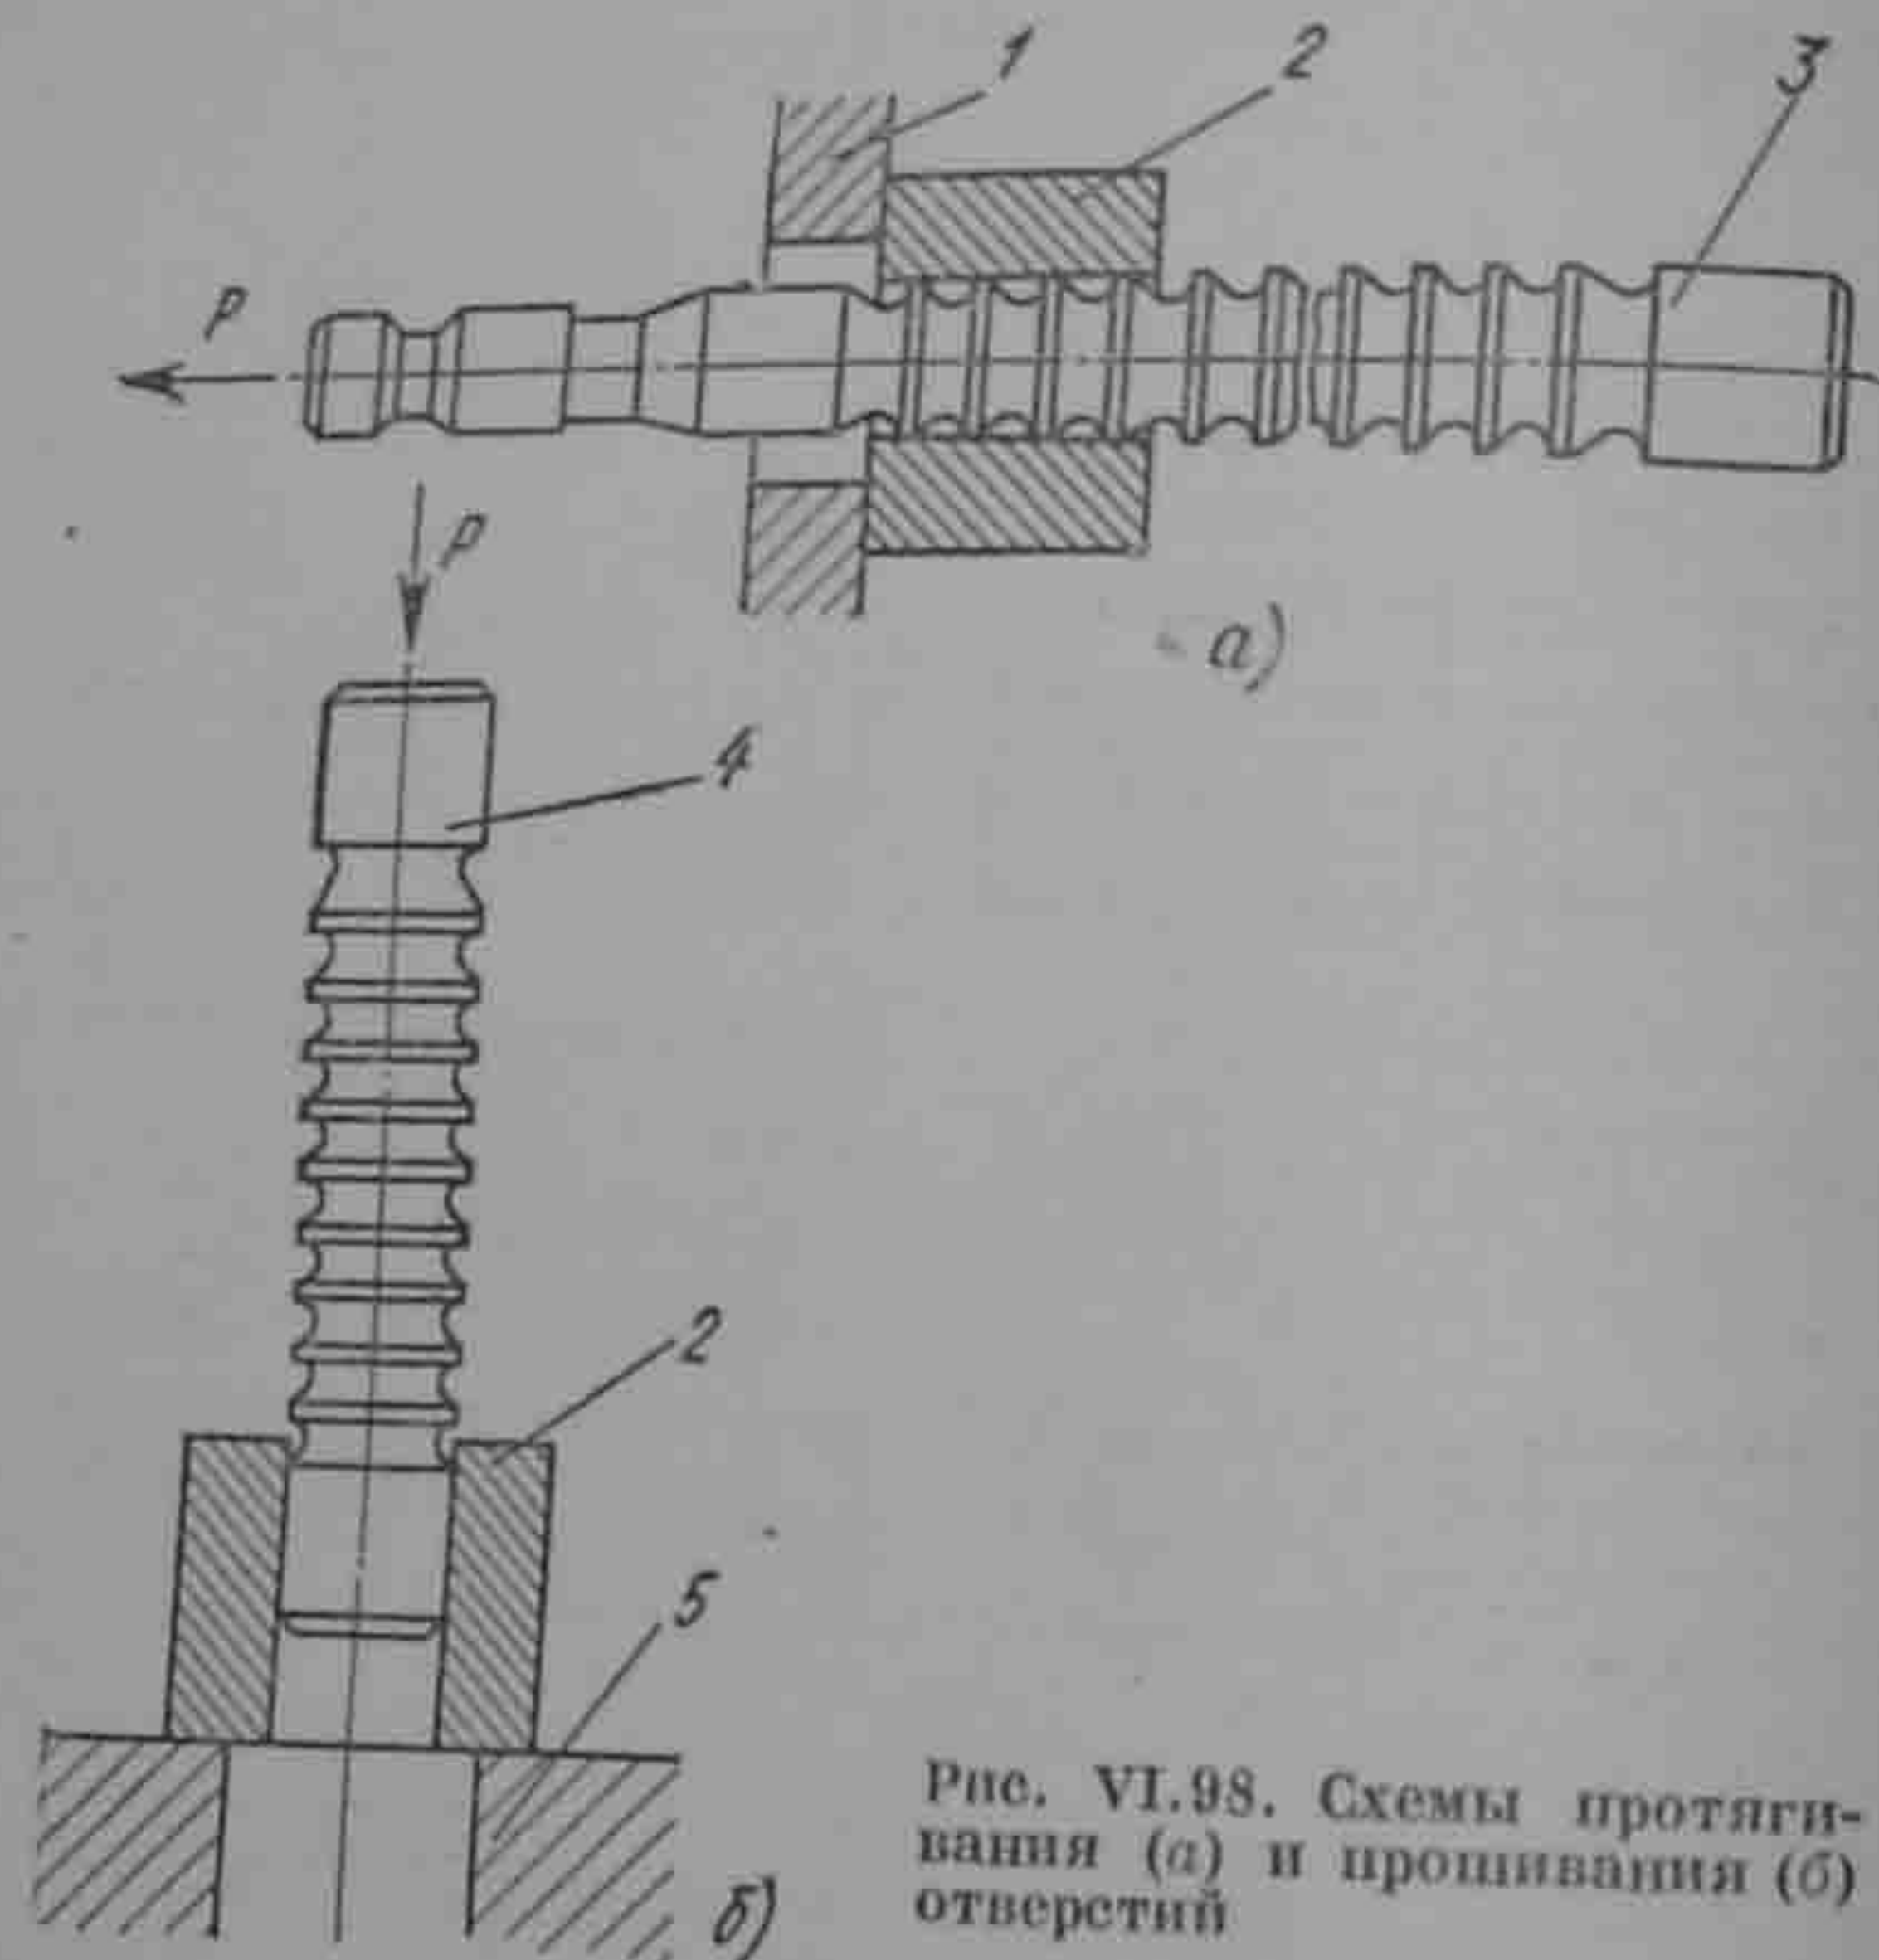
Схемы протягивания (а) и прошивания (б) отверстий
